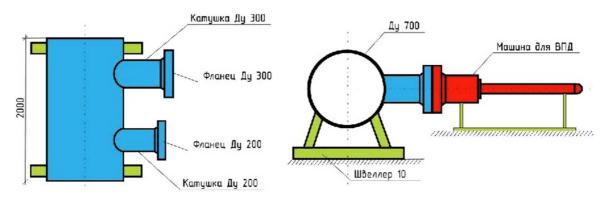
Эскиз испытательного стенда № 1 для стандартных фрез
